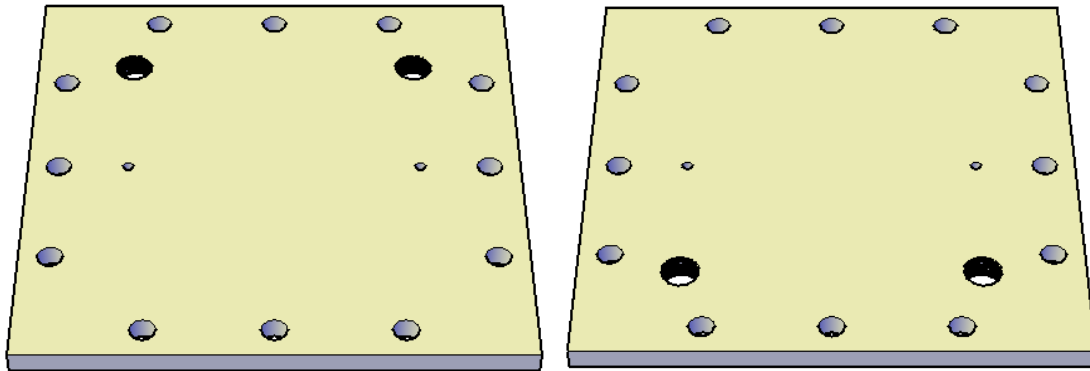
Diseño de tapa inicial en AutoCAD.
